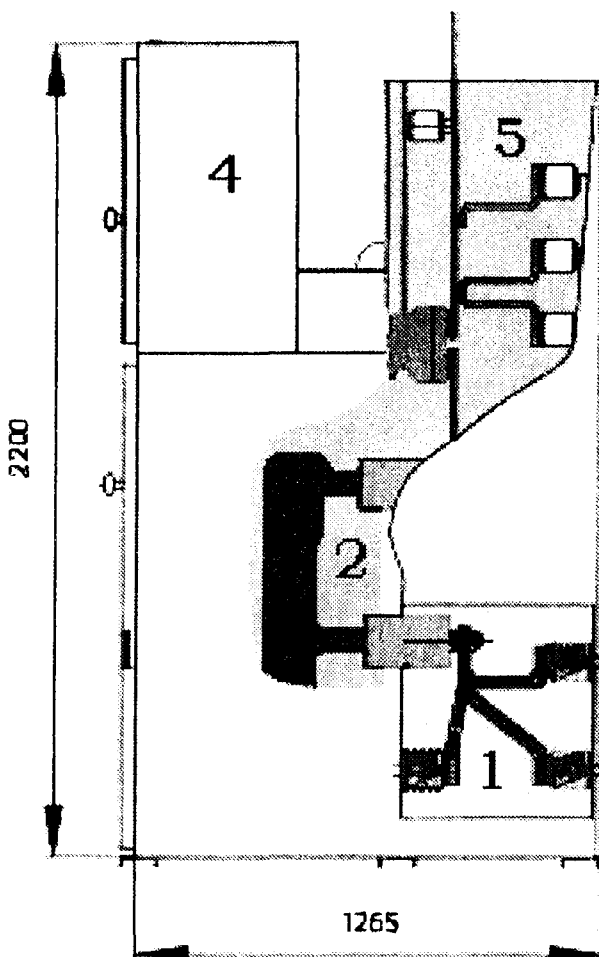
Общий вид и габаритные размеры шкафа К-104М
